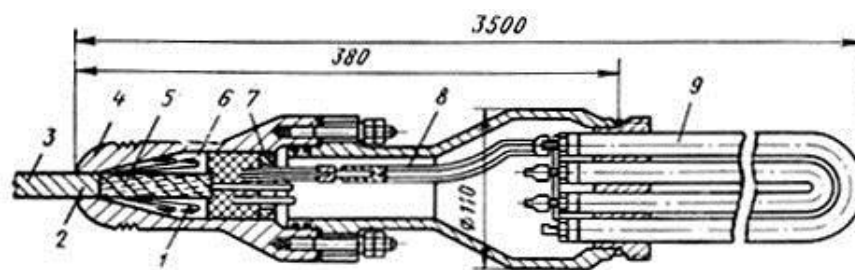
Скважинный электронагреватель: 1 - крепление кабеля; 2 - проволочный бандаж; 3 - кабель-трос; 4 - головка нагревателя; 5 - асбестовая оплетка; 6 - свинцовая заливка; 7 - нажимная гайка; 8 - клеммная полость; 9 - нагревательные трубки.
